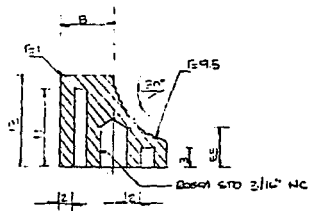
FIGURA DE	<b>DESOLDADOR SOLDEX</b>	ESC	1/1
